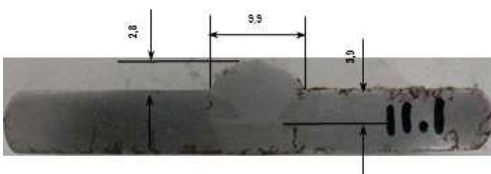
Macrografias com altura do reforço (r), largura do cordão de solda (b) e a penetração das soldas com CO₂+2%H₂.
